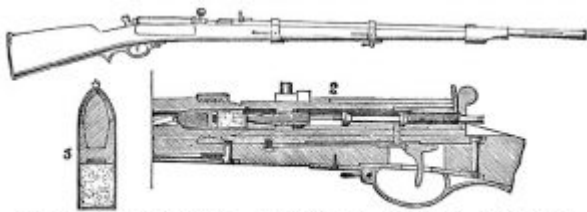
Fusil à aiguille prussien. — 1. Fusil entier. — 2. Section. — 3. Cartouche.
